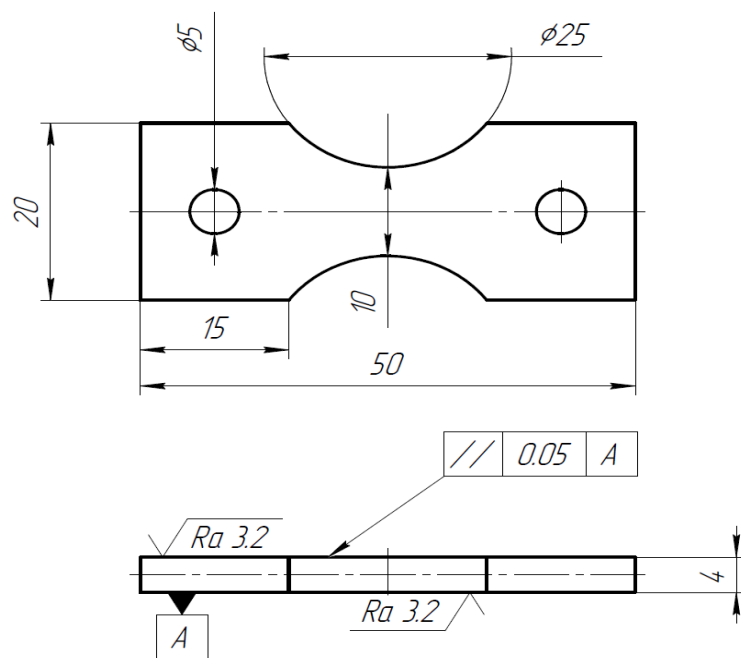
Геометрия и основные размеры образца для испытаний на растяжение
